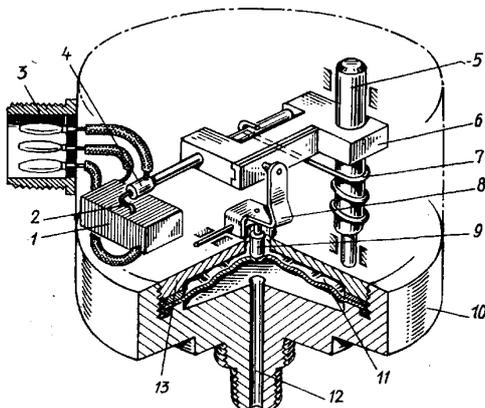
Потенциометрический датчик давления 1 - потенциометр; 2 - щетка; 3 - вилка; 4 - щеткодержатель; 5 - ось поводка; 6 - поводок; 7 - возвратная пружина; 8 - качалка; 9 - шток; 10, 13 - основания; 11 - мембрана; 12 - штуцер
